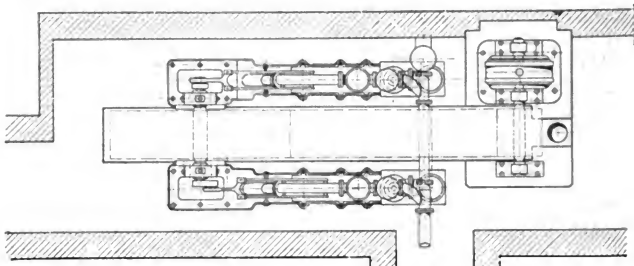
, Pumpenantrieb. Grundriss.
